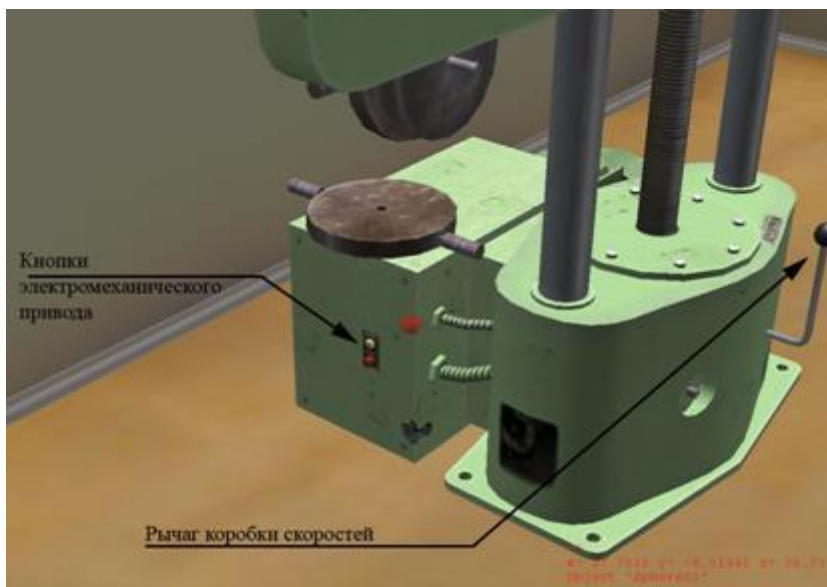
Кнопки электромеханического привода и рычаг коробки скоростей
